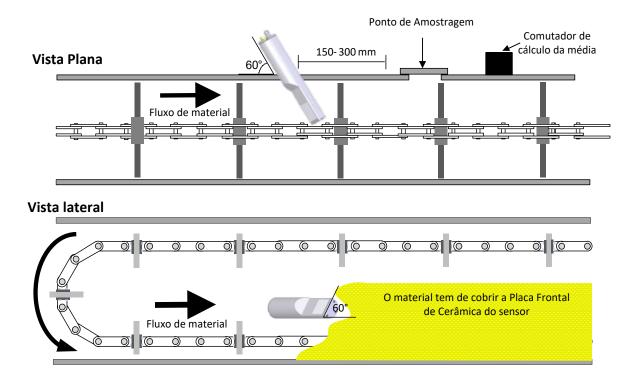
Montagem do Hydro-Probe num Transportador em Massa
